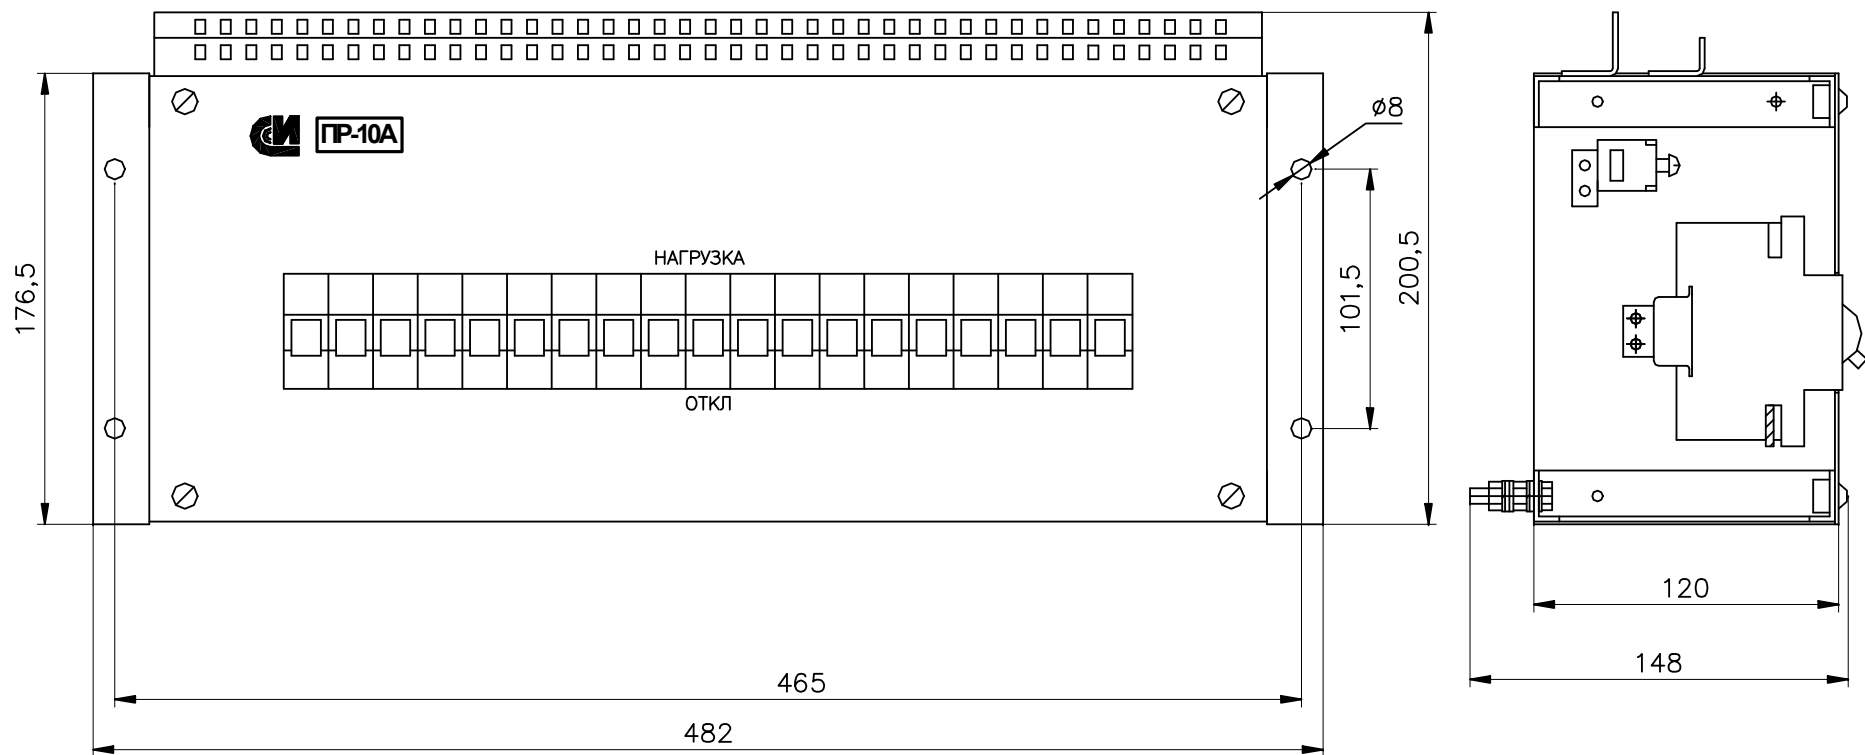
Общий вид и габаритно-присоединительные размеры панели ПР-10А
